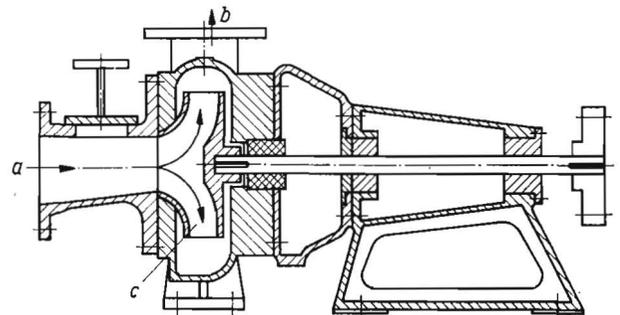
Dickstoffpumpe Typ KR D VEB Pumpenwerk Erfurt mit horizontaler Welle und Schlauchrad. a Zuflußleitung, b Druckleitung, c Schlauchrad
